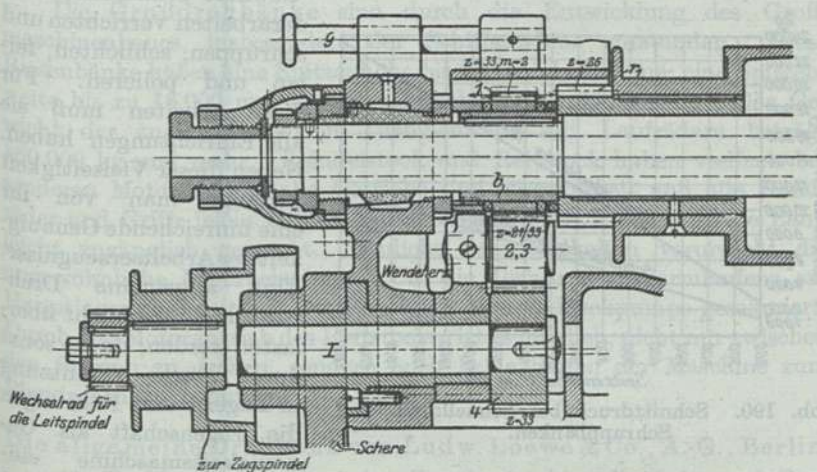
Wendeherz für gewöhnliches und steiles Gewinde. Gebr. Böhringer, Göppingen.
